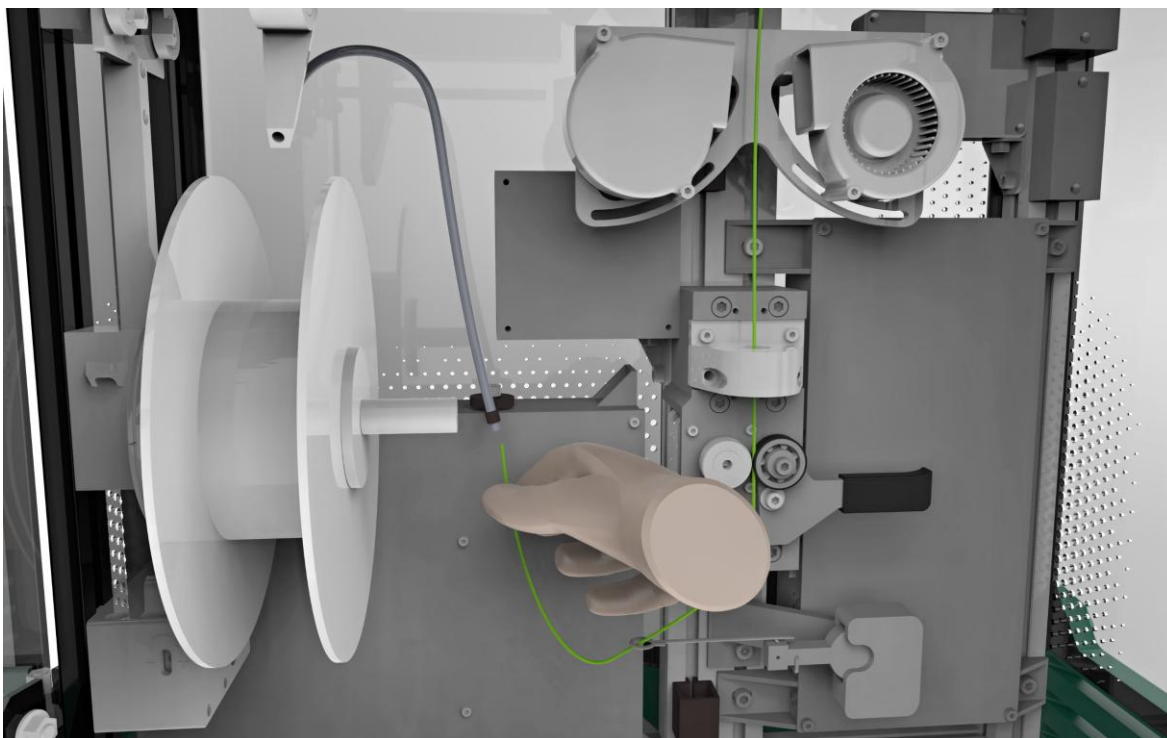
Detail ovládání s páčkou napínací kladky
